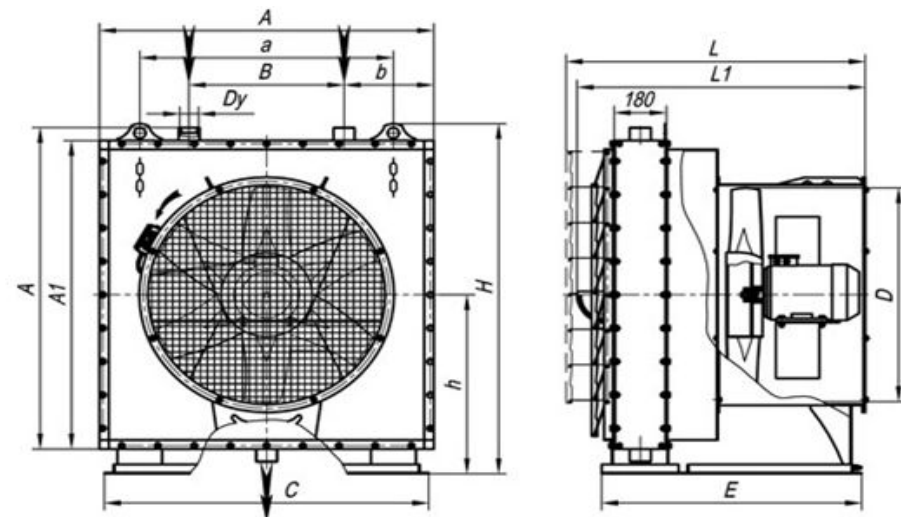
Габаритные размеры агрегата воздушно-отопительного АО2 №10-25П на базе воздухонагревателя КПСк.
